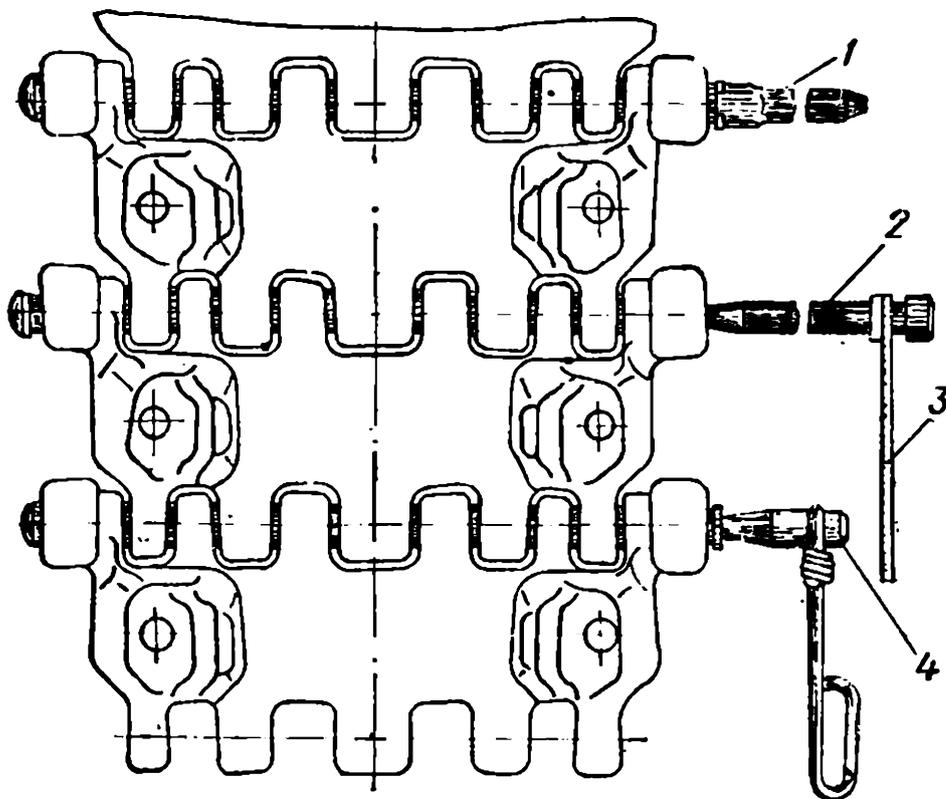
Установка комплекта приспособлений для замены пальцев гусеницы с открытым шарниром:
